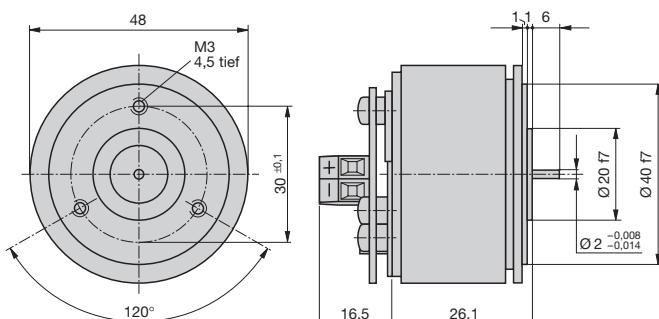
KINAX 2W2 mit Standard-Antriebswelle nur vorn, Ø 2 mm, Länge 6 mm. Anschlussvariante mit Schraubklemmen.
